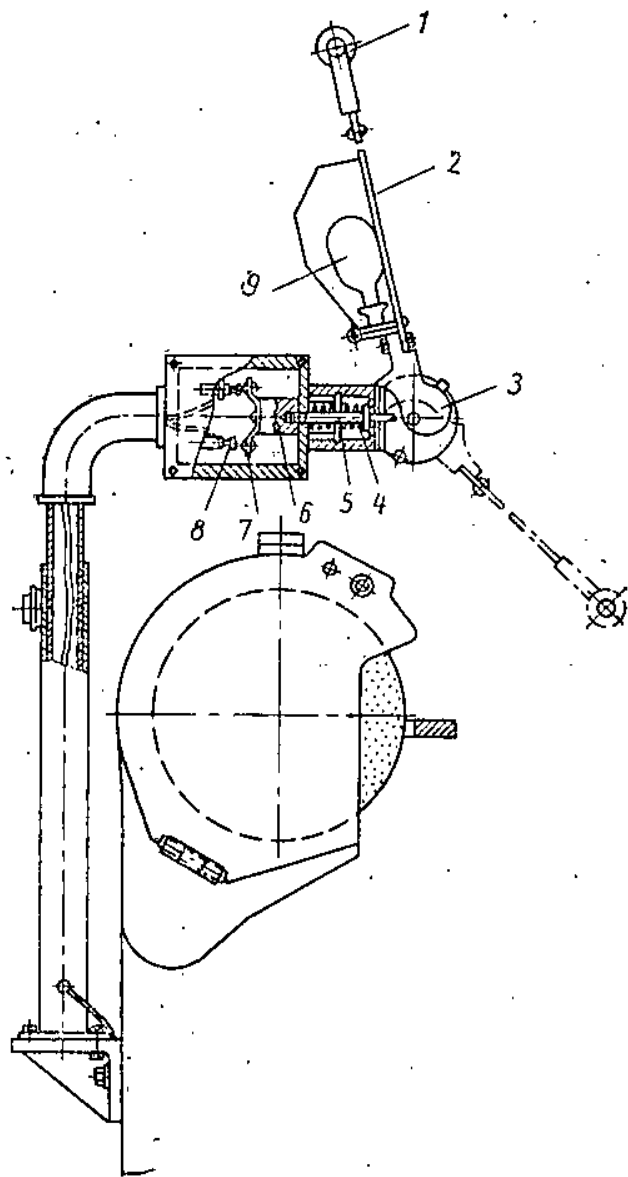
Защитный блокировочный экран заточного станка ЛИОТ
